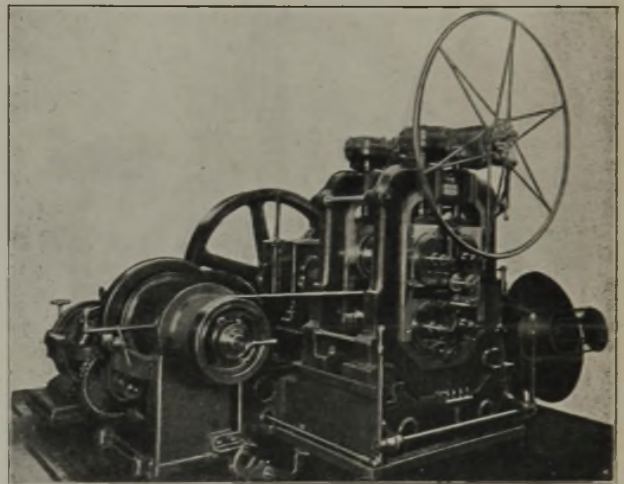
Mit Rollenlagern ausgerüstetes Sechswalzengerüst.
